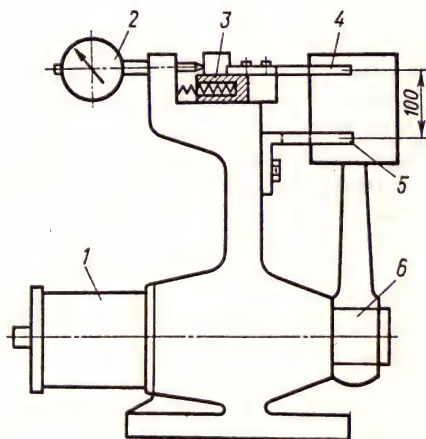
Приспособление для контроля шатунно-поршневого комплекта в сборе
